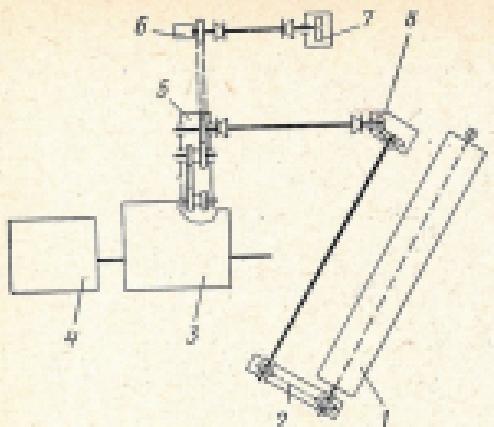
Кинематическая схема плужно-щеточного оборудования ПМ-130:
